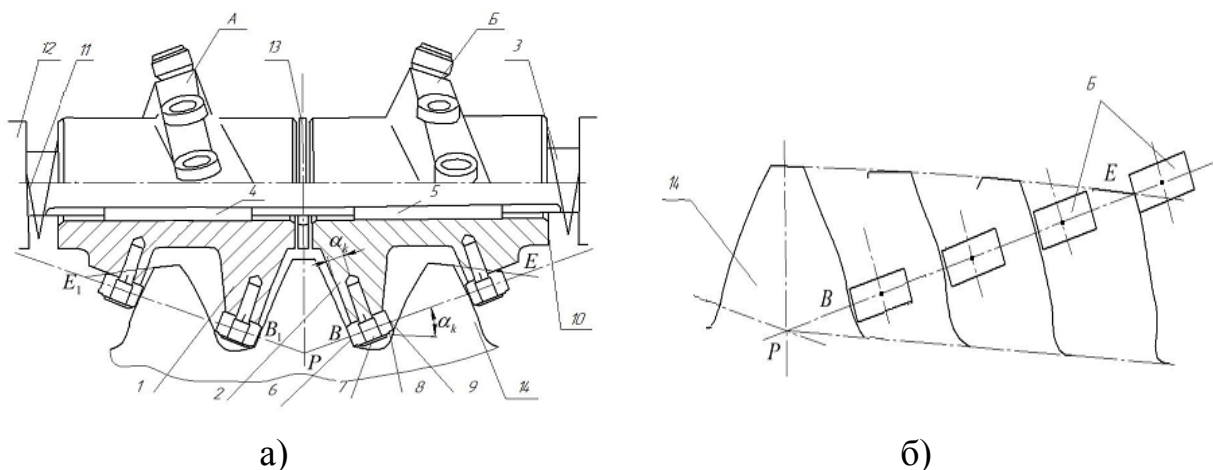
Черв'ячний накатник для обробно-зміцнювального оброблення зубчастих коліс ППД: а - загальний вид інструменту; б - схема взаємодії накатного елемента з бічною поверхнею зуба колеса
